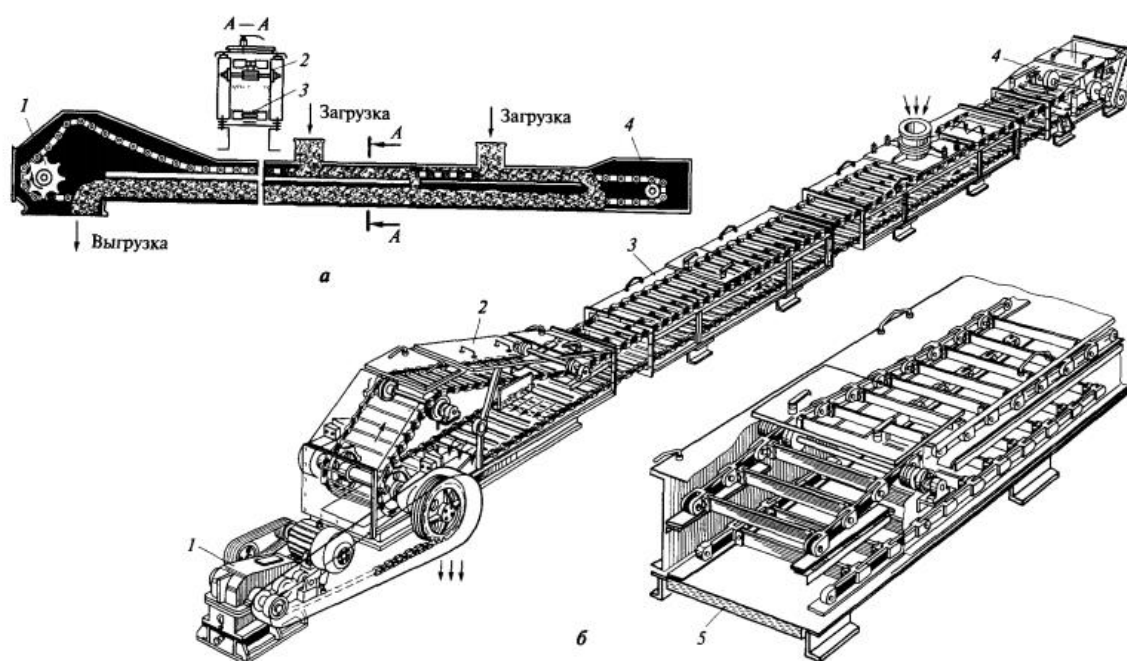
Скребокковый конвейер со сплошными низкими скребками
